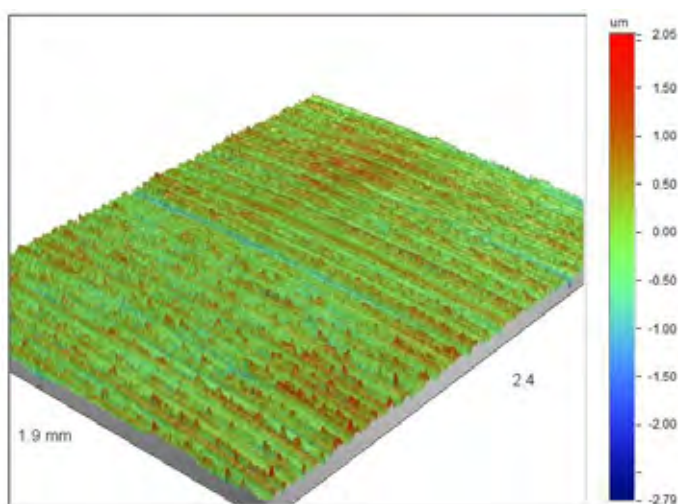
Representação tridimensional da superfície do material GUF, usinado sob condição C1.
